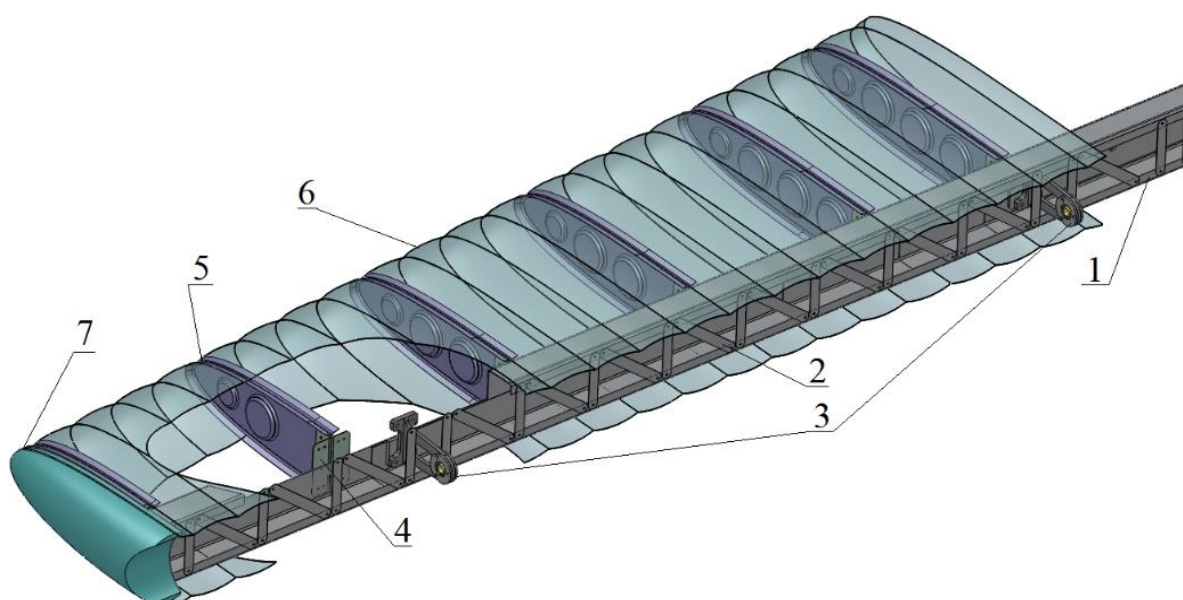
Конструкция стабилизатора: 1 – лонжерон, сборной конструкции; 2 – набор распорок; 3 – узлы навески рулевых поверхностей; 4 – уголок; 5 – пластиковая нервюра; 6 – волнистая обшивка; 7 – концевой обтекатель
